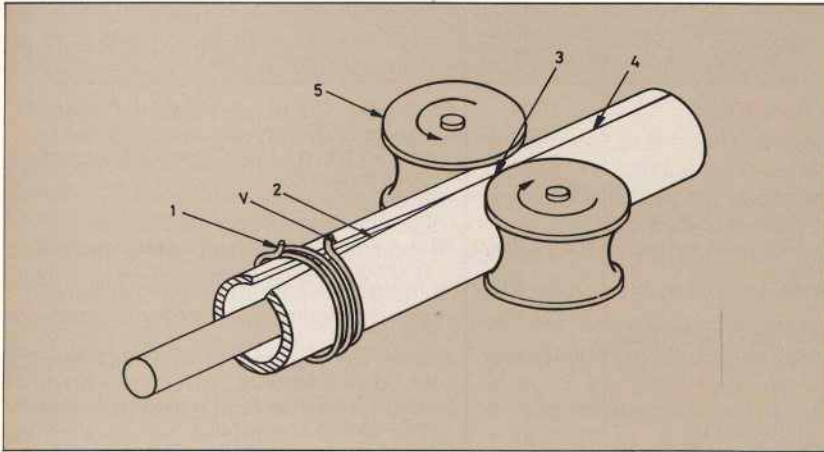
Fabricación de tubos por soldadura mediante inducción de la chapa de acero bajo en carbono: 1) cable inductor; 2) corriente eléctrica; 3) punto de soldadura; 4) línea de soldadura; 5) laminadores; v) fuerza electromotriz.
